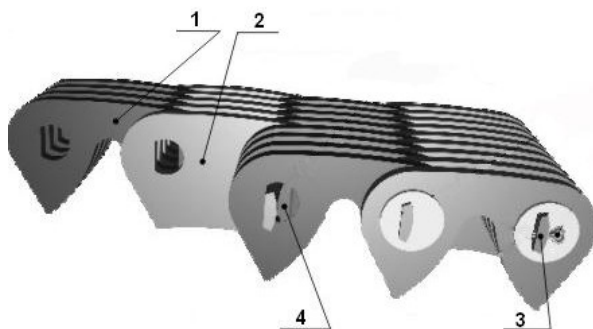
Зубчатая цепь: 1 – рабочая пластина;
